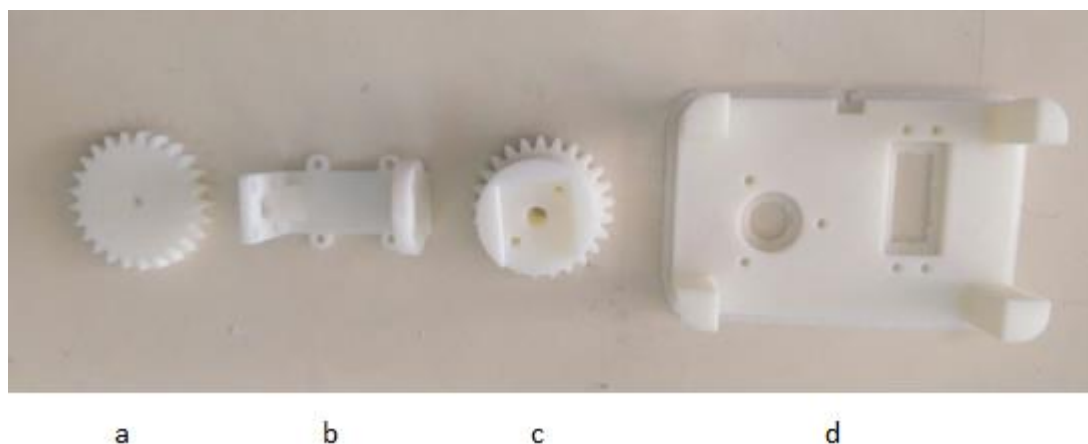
Componentes internos impresos; (a) Engrane del motor, (b) Soporte del sensor LIDAR (c) Engrane del sensor y (d) Estructura interna de anclaje para el motor y el colector
